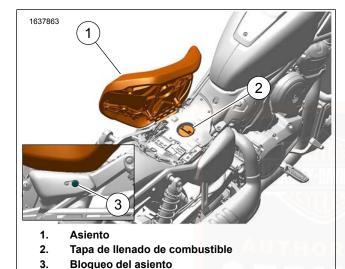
Llenado de combustible (tanque de combustible debajo del asiento)
